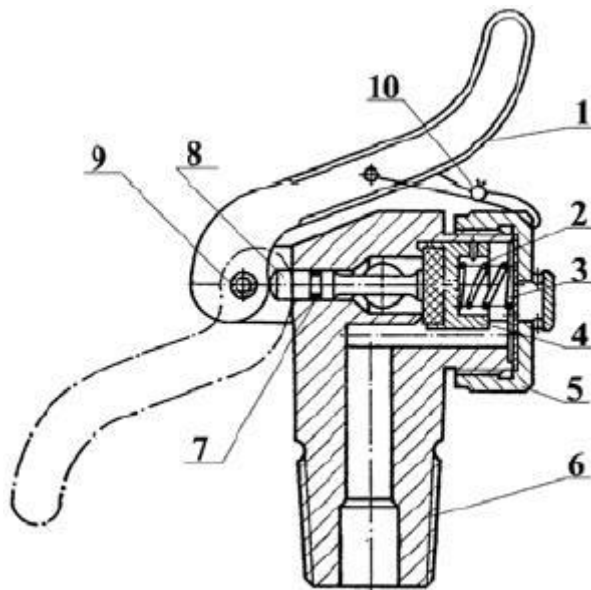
устройство и принцип действия запорно-пускового устройства (ЗПУ) рычажного типа. Цифрами на рисунке обозначены: 1 – рычаг; 2 – пружина; 3 – прокладка; 4 – седло клапана; 5 – гайка; 6 – хвостовик; 7 – манжета; 8 – шток клапана; 9 – ось рычага; 10 – пломба.
